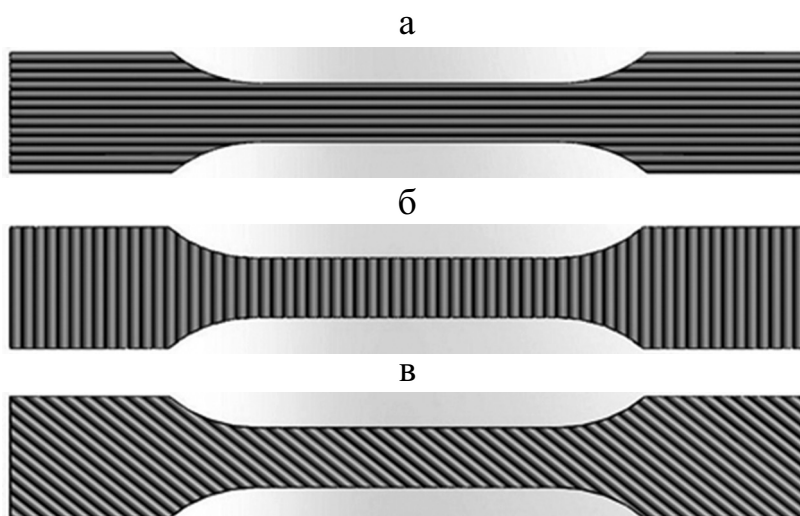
Внешний вид образцов, изготовленных разными способами 3D-печати: *а* — продольное направление печати; *б* — поперечное; *в* — под углом 45°.
